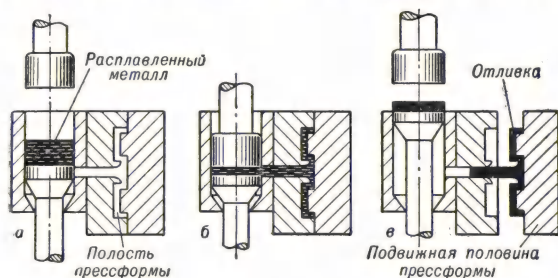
Схема литья под давлением: а — жидкий металл заливается в камеру сжатия; б — момент запрессовки жидкого металла в полость пресс-формы; в — отливка затвердела и может быть извлечена из пресс-формы.
